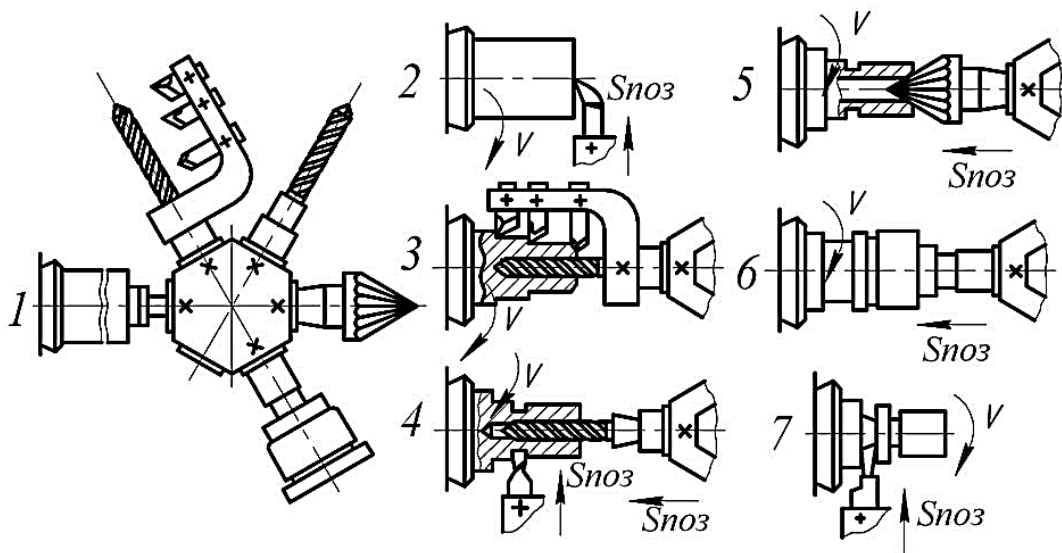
Схеми обробки поверхонь заготовки на револьверному верстаті:
